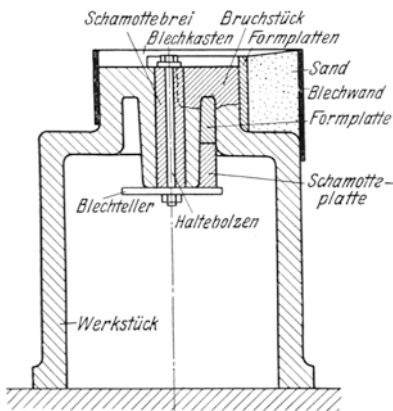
Einförmung eines Warmschweißstücks mit Formkasten.
